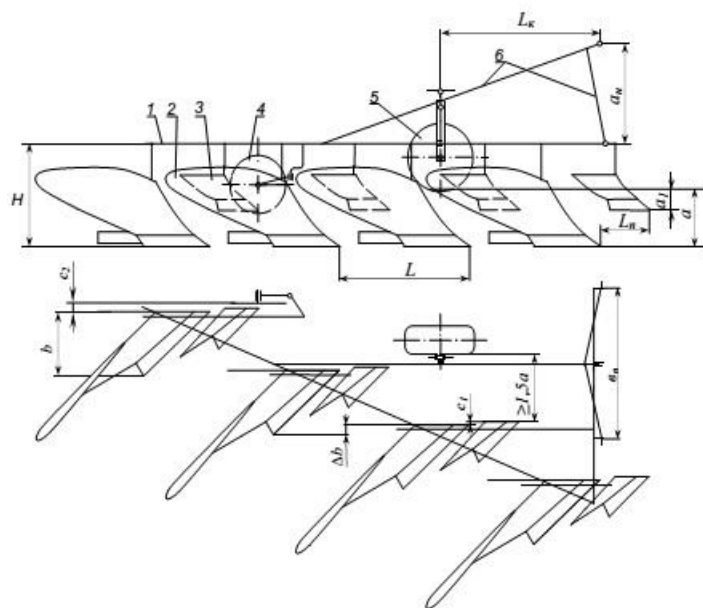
Принципова схема начіпного плуга: 1 – рама; 2 – корпус; 3 – передплужник; 4 – дисковий ніж; 5 – опорне (польове) колесо; 6 – навіска
